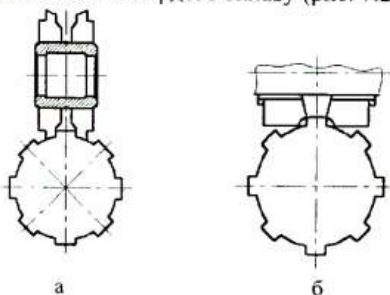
Фрезерування шліців фасонними фрезами: а – попередня обробка; б – чистова обробка бічних поверхонь шліців
